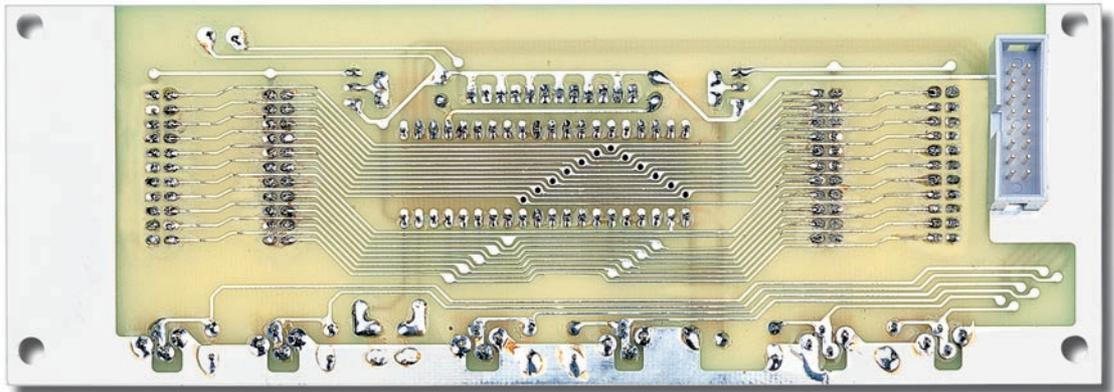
Photo d'un des prototypes de la platine LED et pousoirs, vue côté soudures où l'on montera CONN1 repère-détrompeur en U évidé vers la gauche.
